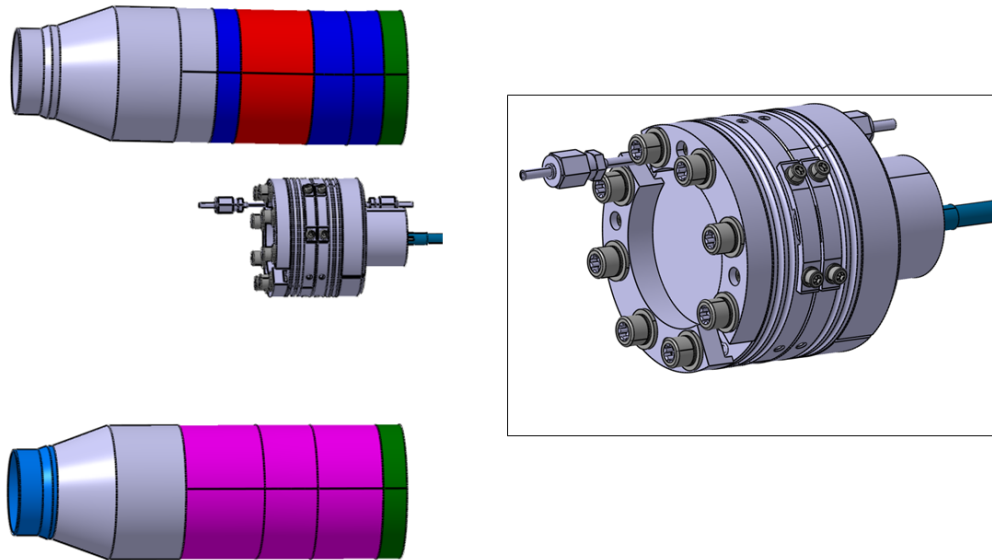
Divertor VUV 분광기의 Vacuum Pipe 영역 부분. 파이프 일부분은 Angle Pipe임. Vacuum Flange는 Double Metal Seal 사용. (참고문헌 [25])
